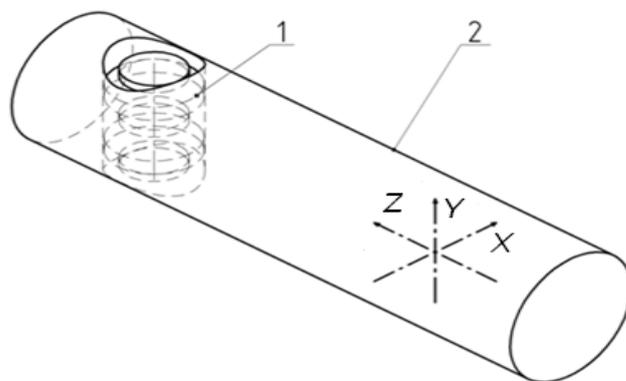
Общий вид измерительного зонда: 1 – ВТП, 2 – корпус
